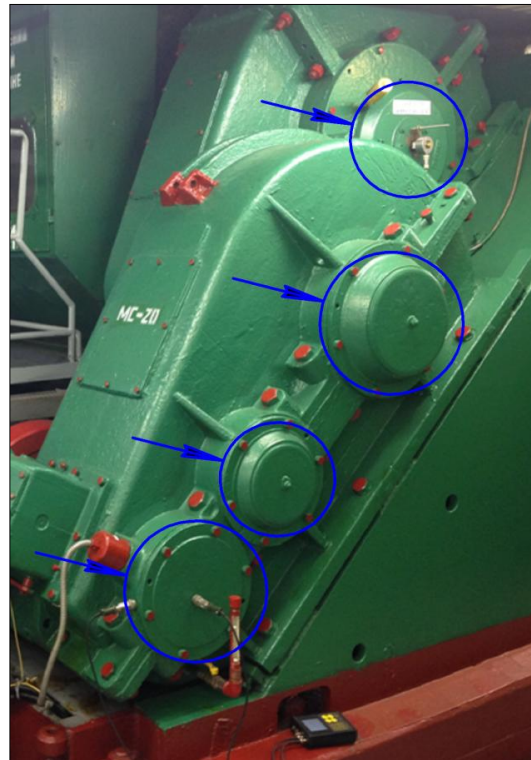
Подшипниковые щиты редуктора и главного вала
